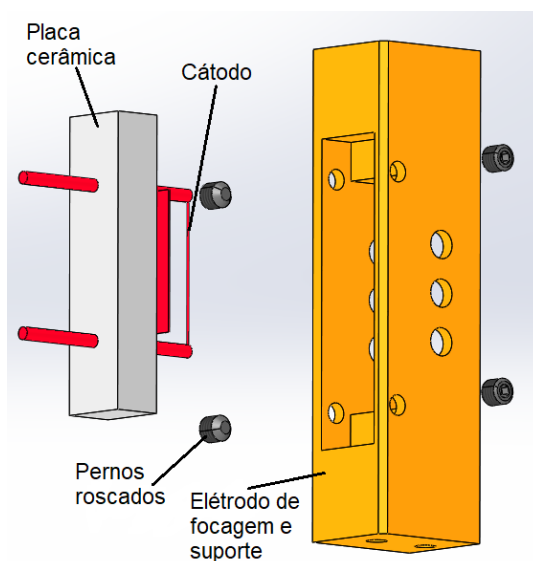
Vista explodida do conjunto de emissão do manómetro cilíndrico.
